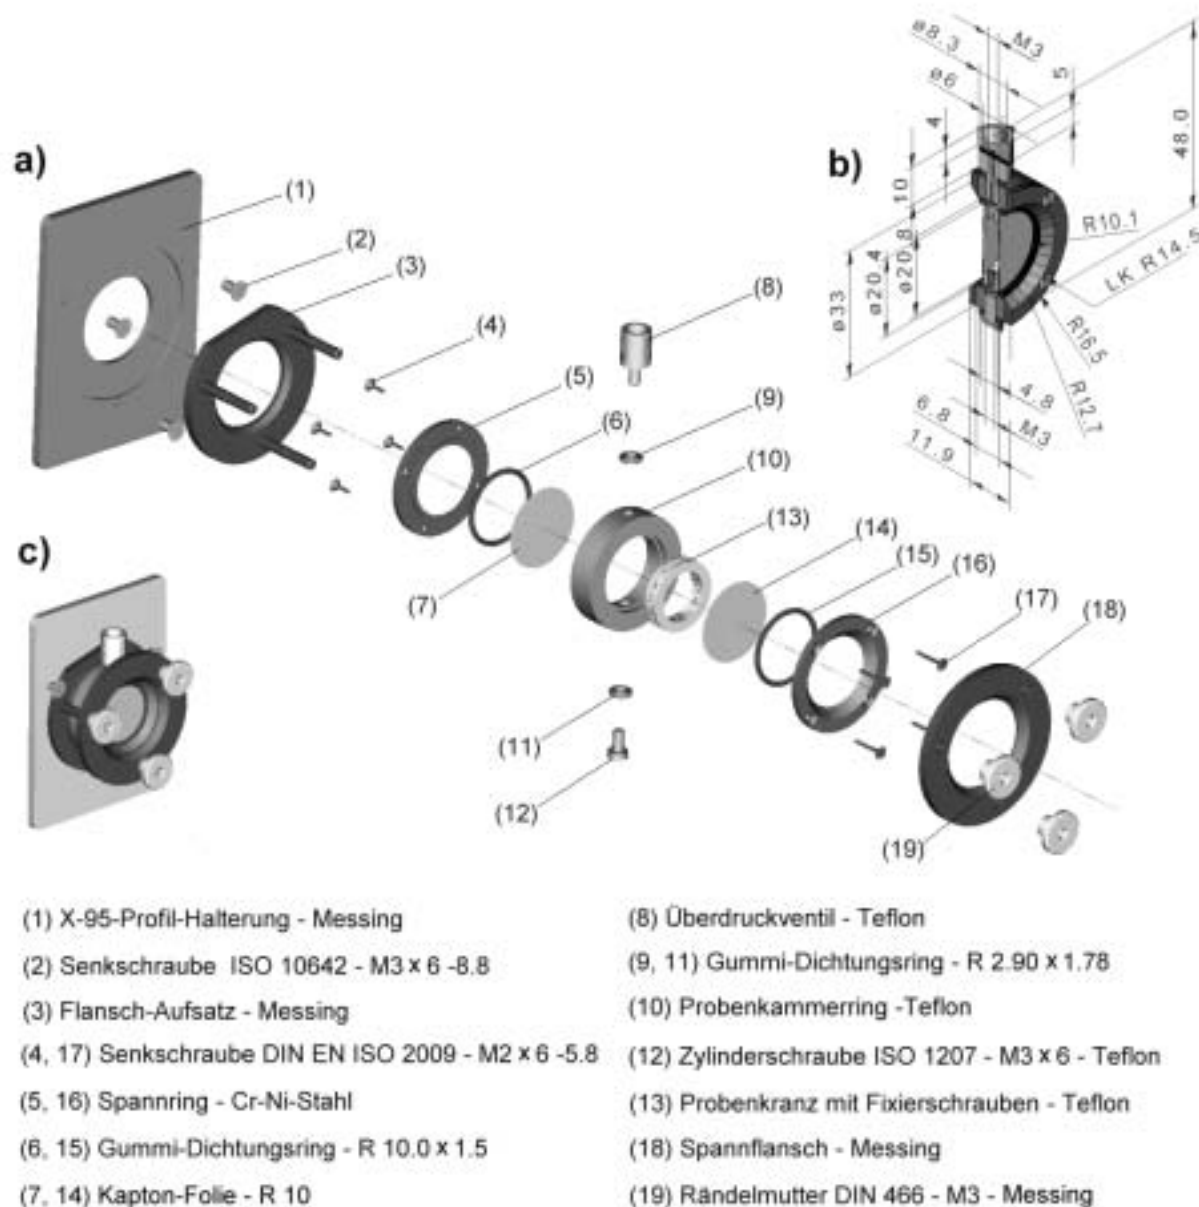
Explosionszeichnung der Probenhalterung (a) und Halbschnitt des Hochtemperaturofens mit Probenhalterung (b).
